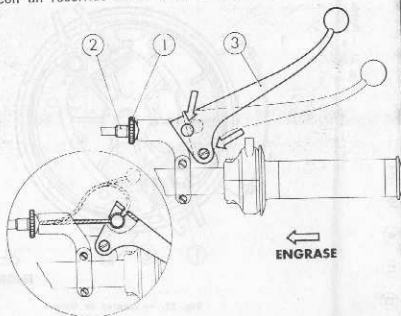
Mando freno delantero. Reglaje y engrase.
